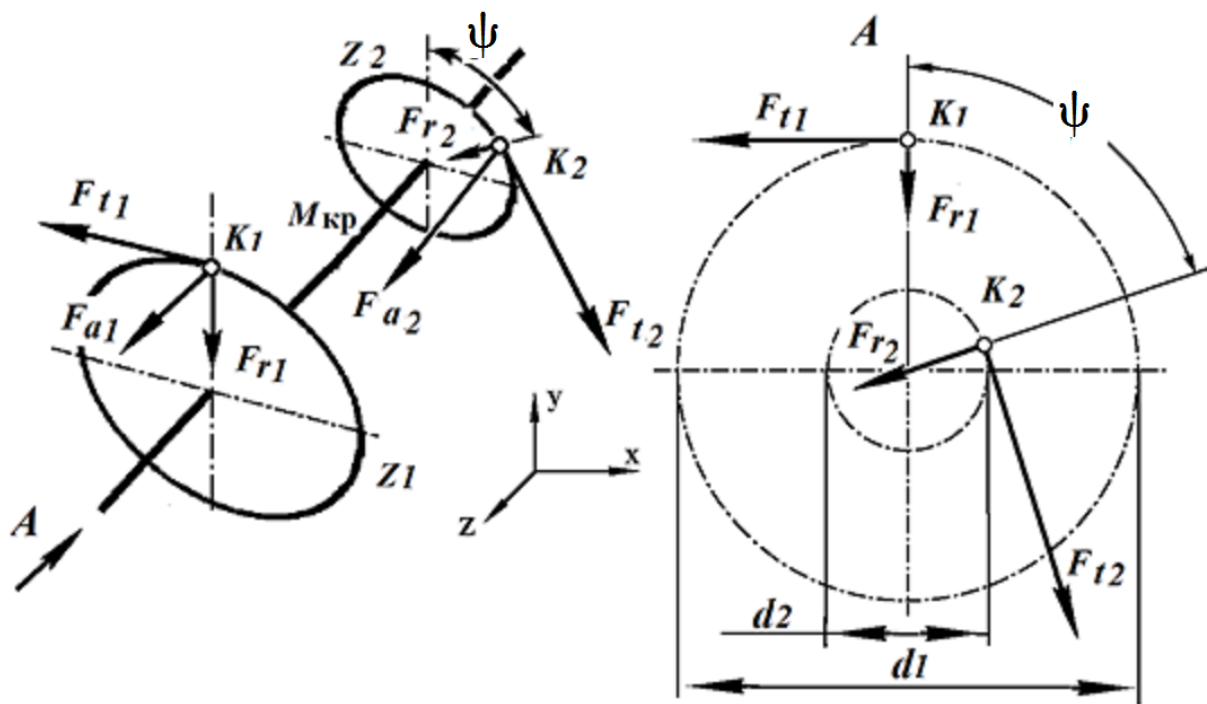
Схема нагружения промежуточного валика многоступенчатой зубчатой передачи
